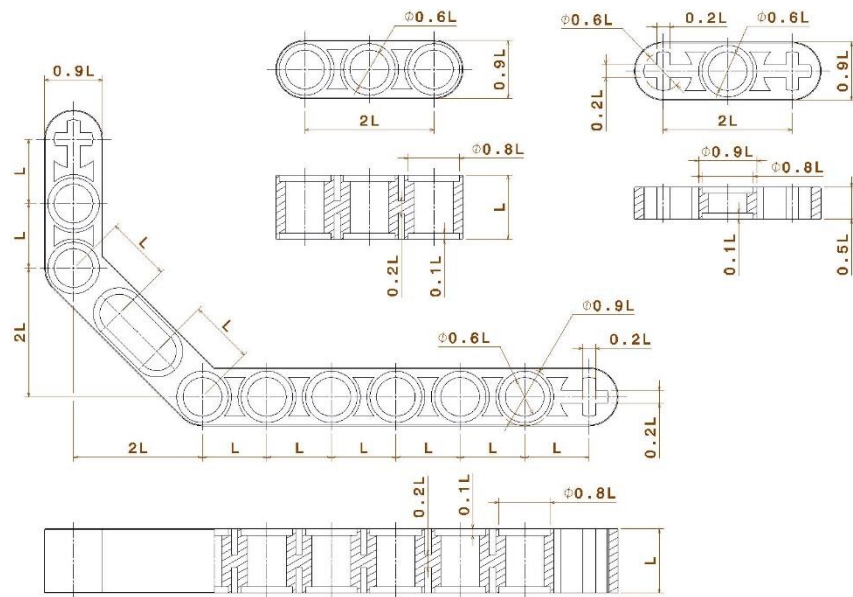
Sistema de referencia para el cálculo dimensional de ladrillos LEGO Parte 1.
